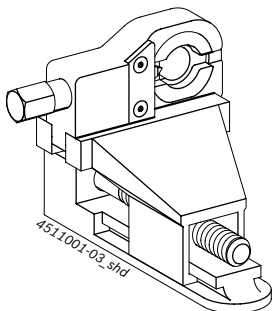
Herramienta de desmontaje en el tornillo de banco
